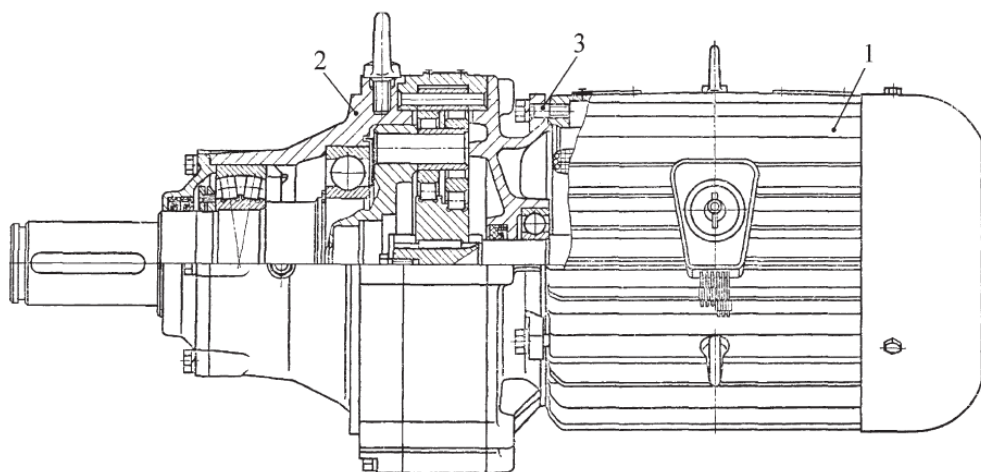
Планетарно-цевочный мотор-редуктор
